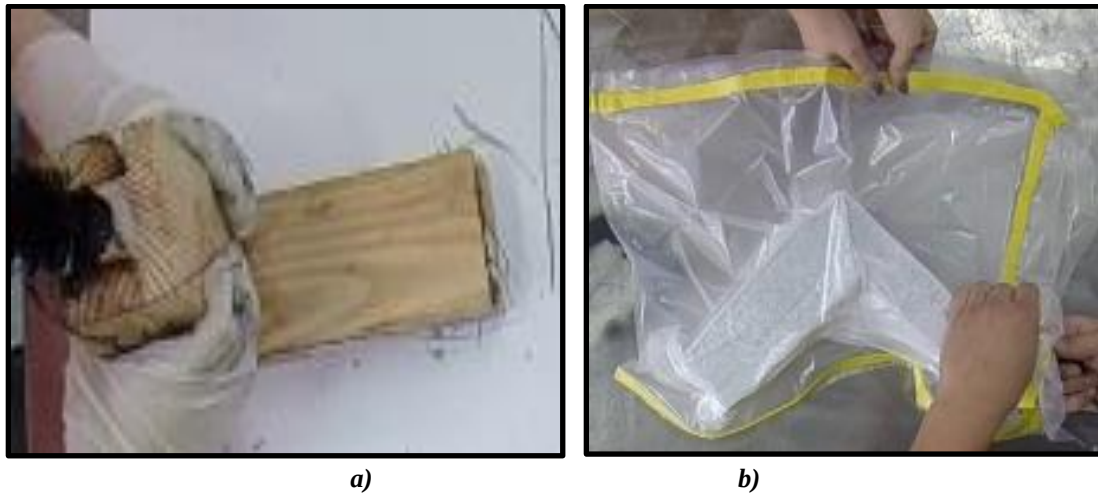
Manufactura de prototipo: a) Cierre de molde; b) Pieza sometida a vacío.
